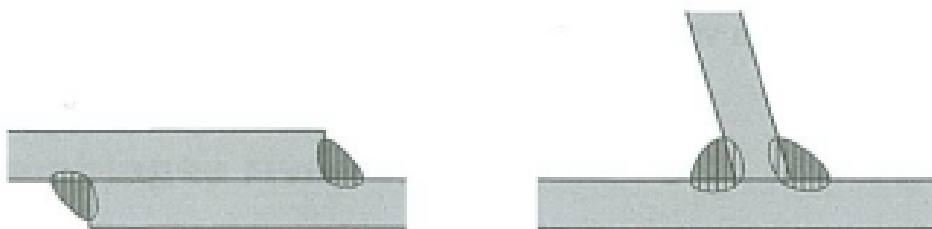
Joint de soudure à cordons d'angle
